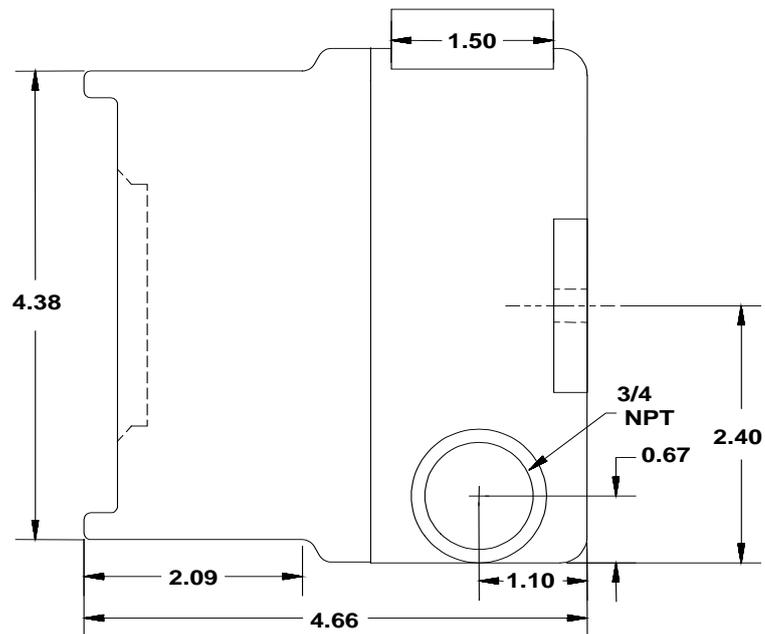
Корпус детектора SS4-AUV/-AUV2 — вид сбоку
